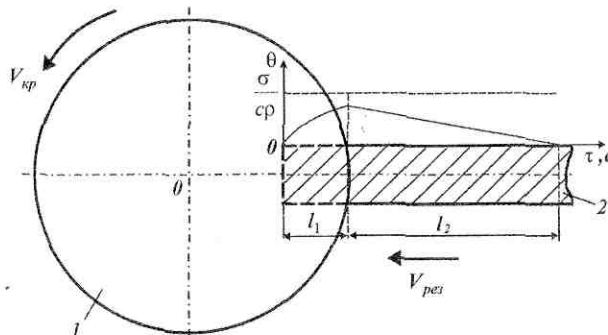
Расчетная схема процесса шлифования прямолинейного образца, движущегося по нормали к рабочей поверхности круга: 1 – круг; 2 – образец
